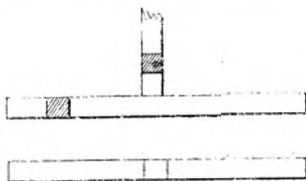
SOUDURE PAR ENCOLLAGE.
